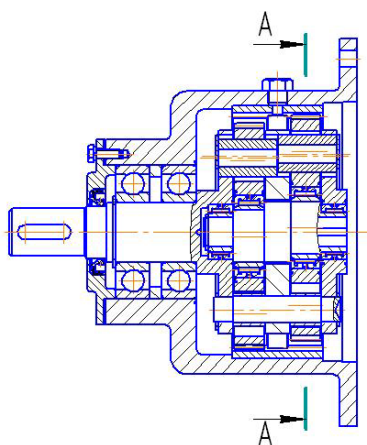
Передача типа 2К-Н с «плавающей» солнечной шестерней и консольными осями сателлитов
